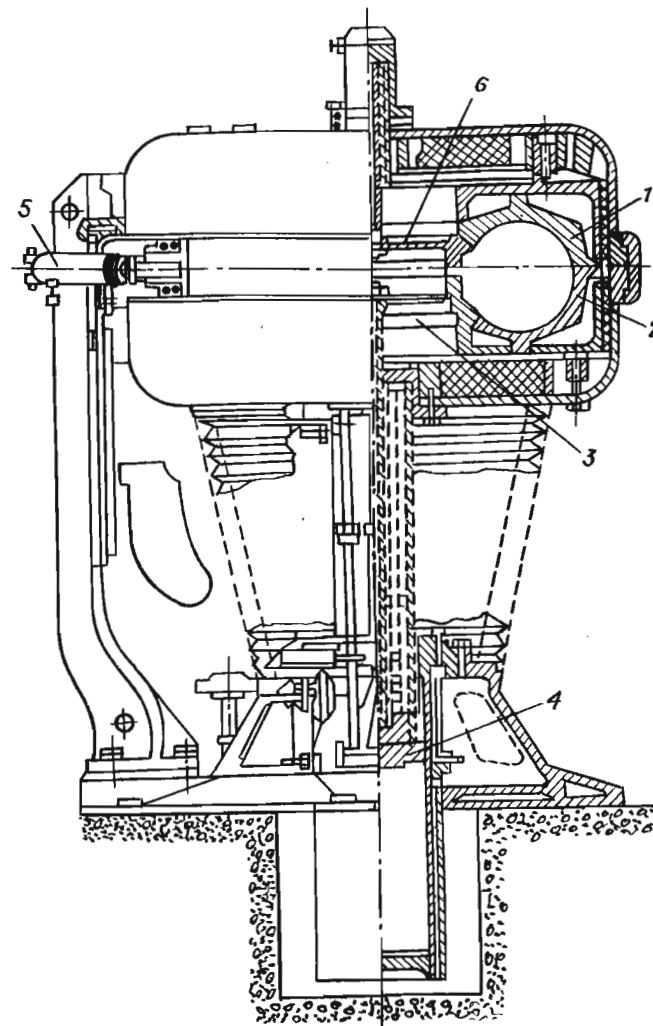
Бескамерный полуавтоматический вулканизатор покрышек:
